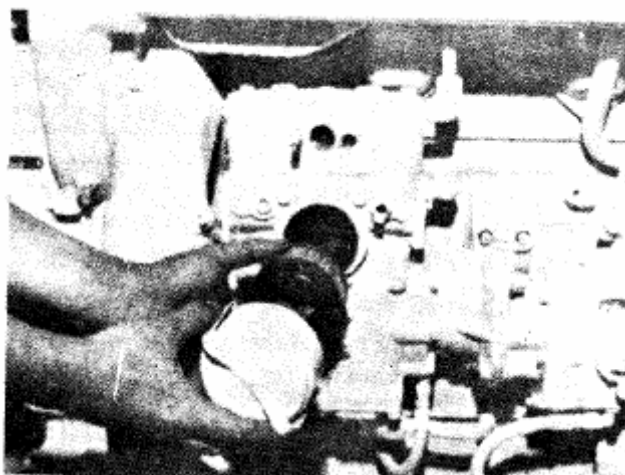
(V41420) Бумажный элемент Bendix - Westinghouse сапуна
